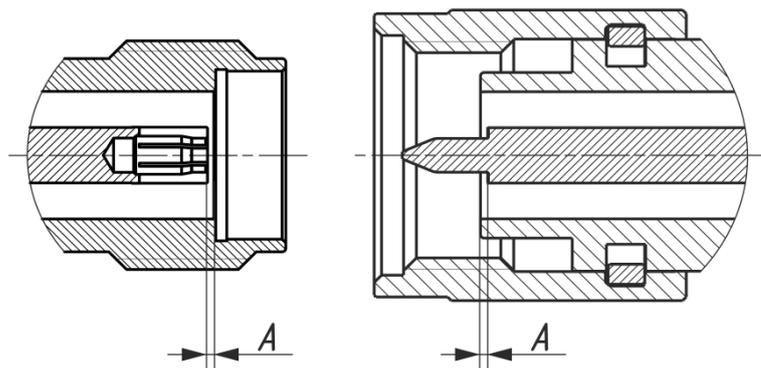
Соединители тип 3,5 мм и IX (розетка и вилка)
